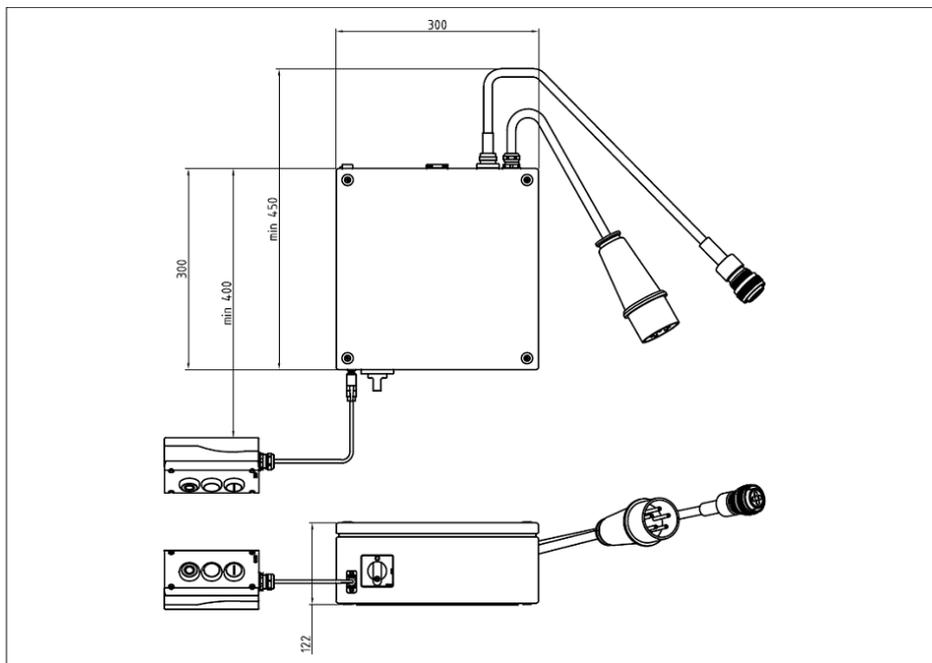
Ingombri di KEH01, KEH02 e KEH02-S
